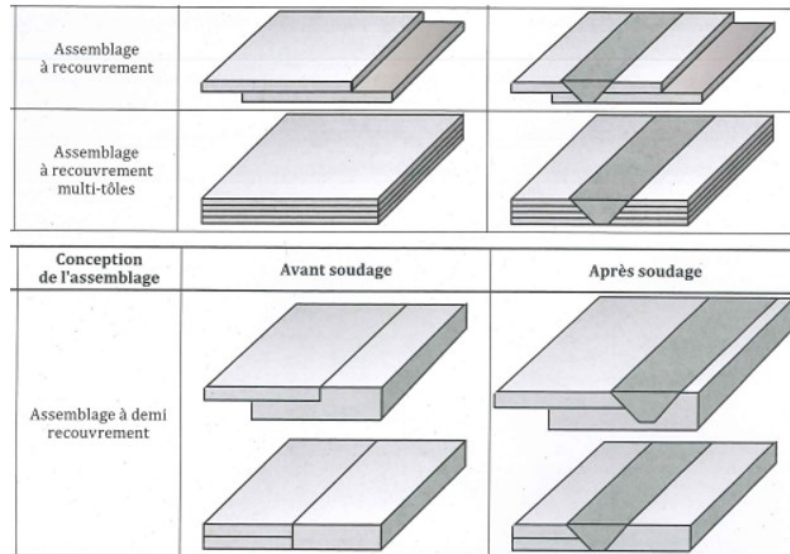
Type de soudure par recouvrement [20]
